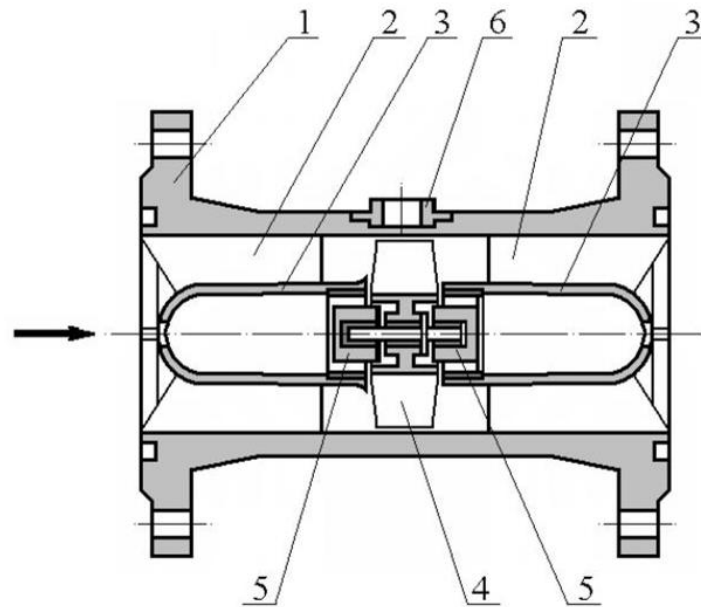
Турбінний перетворювач витрати: 1 – корпус; 2 – струменевипрямляч, 3 – обтікач, 4 – турбінка, 5 – підшипник, 6 – фланець для встановлення індукційного перетворювача
